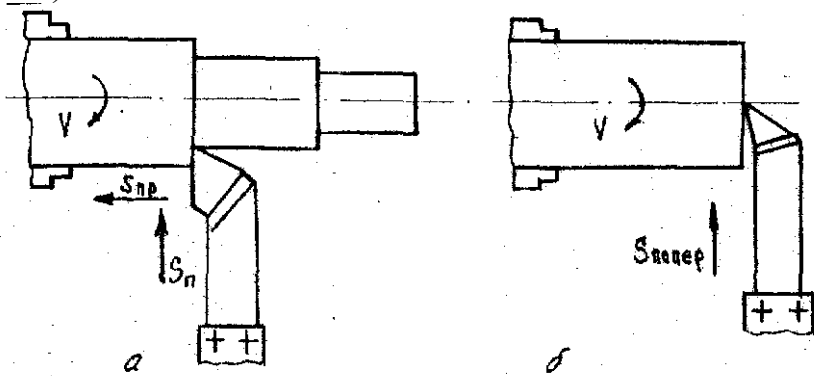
Схеми різання на токарних верстатах: а) обточування ступінчастих валів; б) підрізання торця
